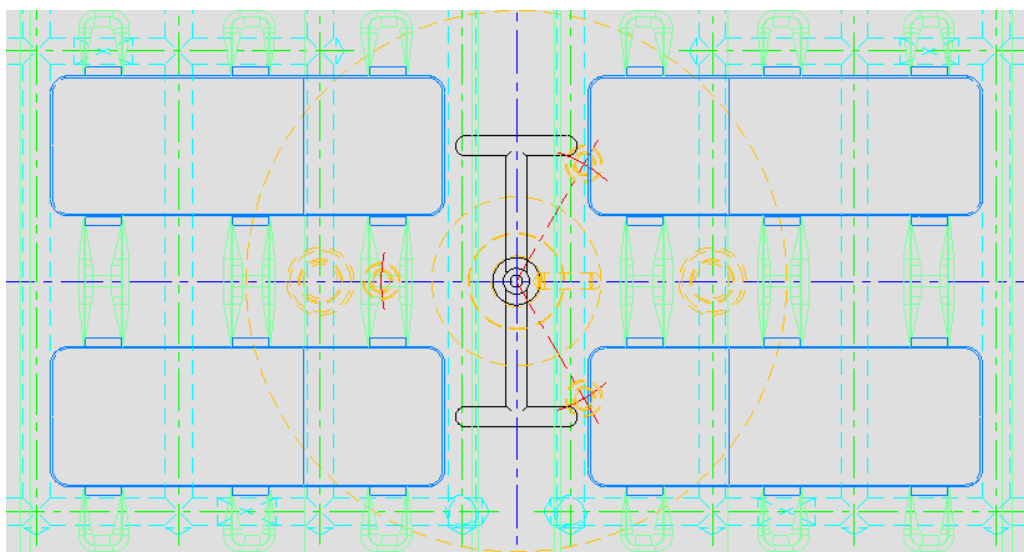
Схема предлагаемого процесса изготовления детали
